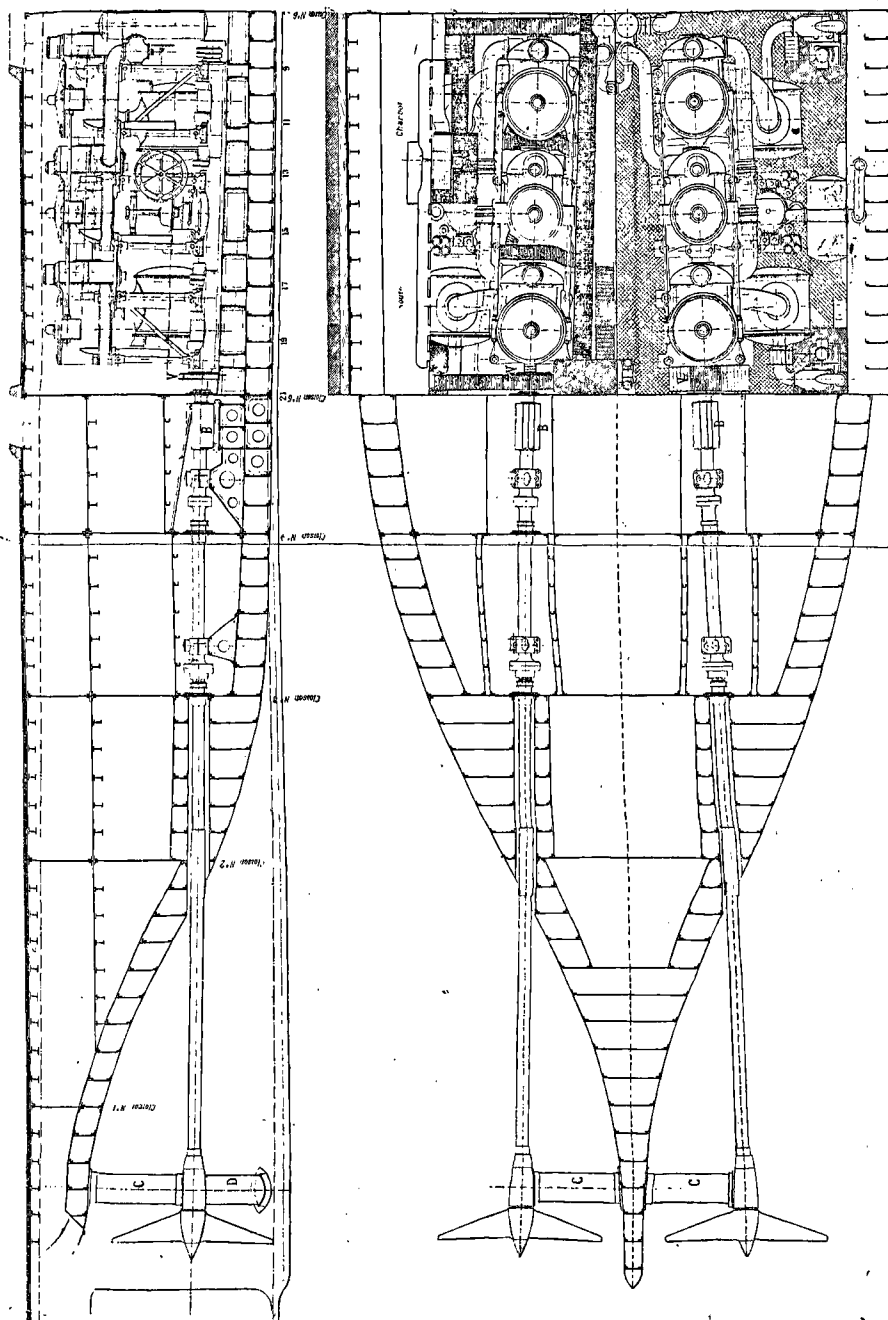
et 582. — *Marceau*, cuirassé. — Coupe longitudinale et plan.
